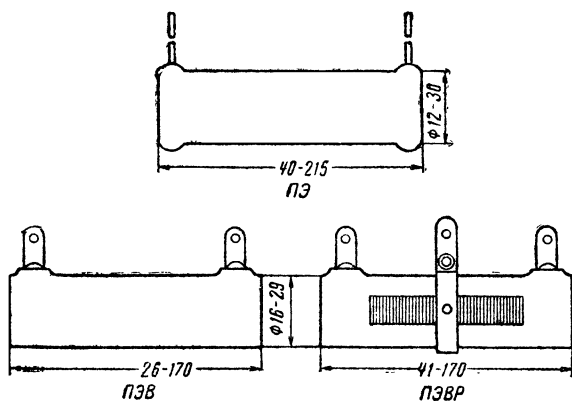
Габаритные чертежи типовых проволочных резисторов.
